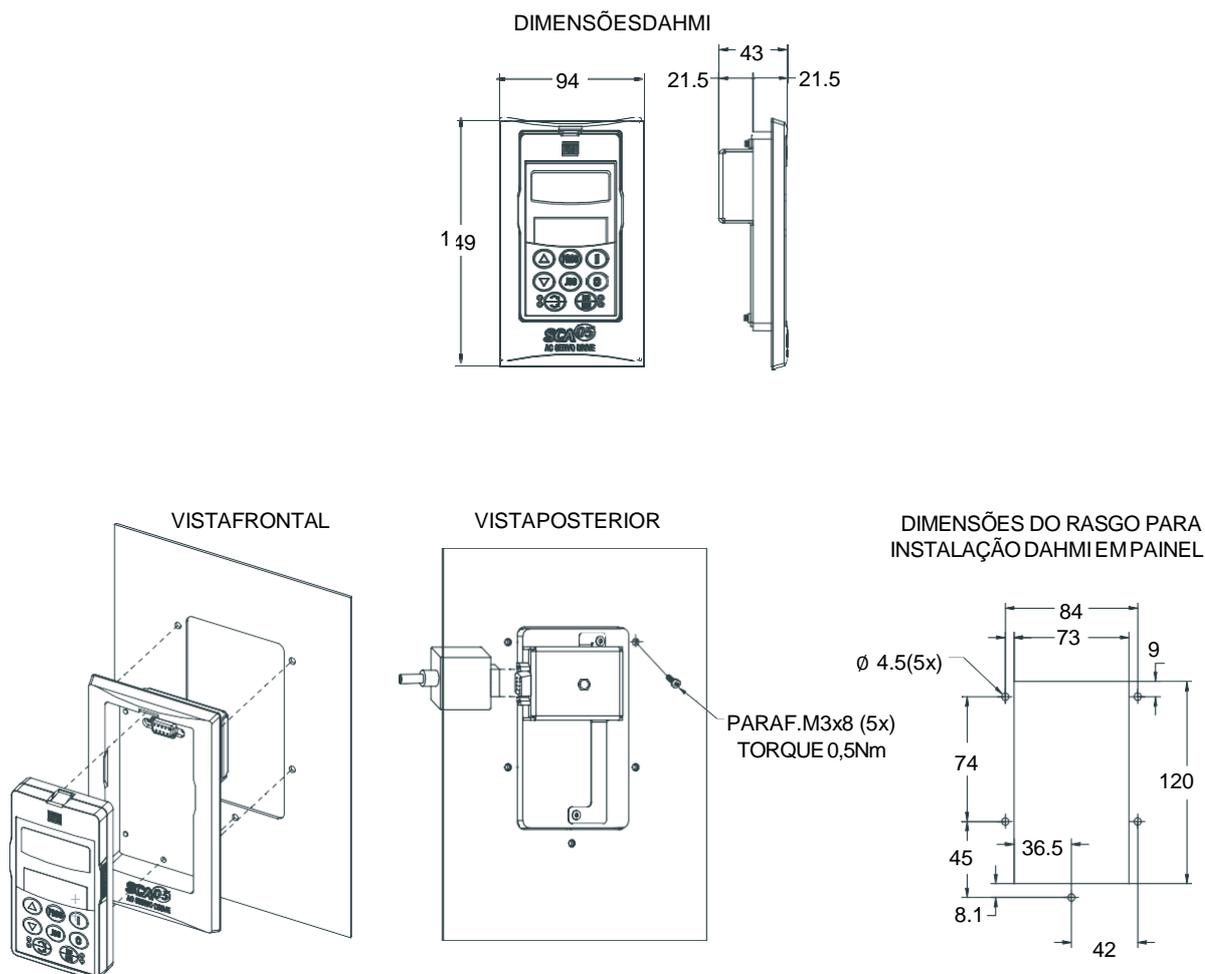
HMI - Dimensões e instalação em painel (mm)
